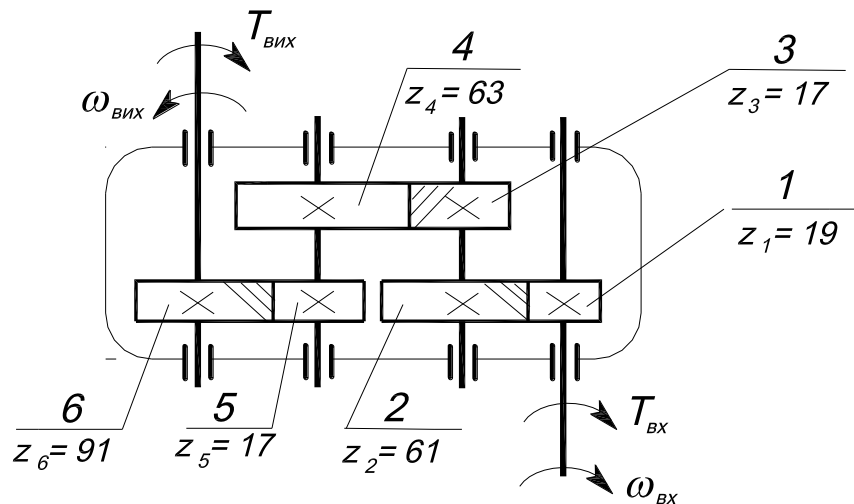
Триступінчастий циліндричний косозубий редуктор. Схема кінематична
